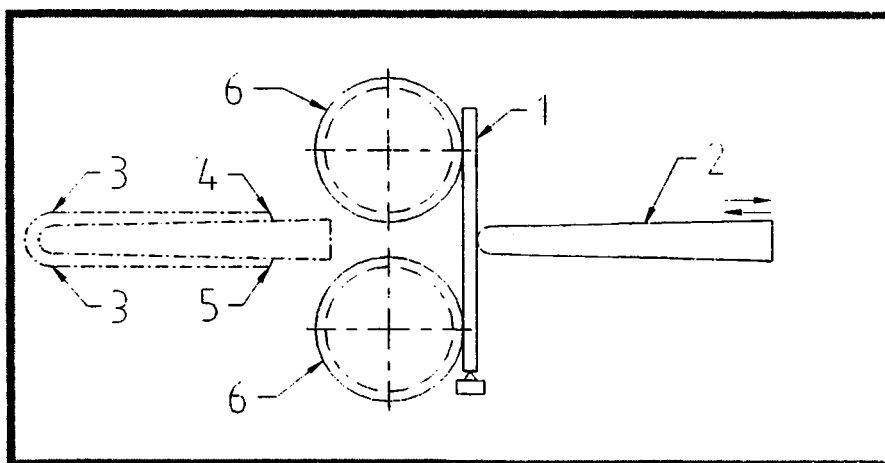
Схемы прокатки или вытяжки с изгибом заготовки [13]
